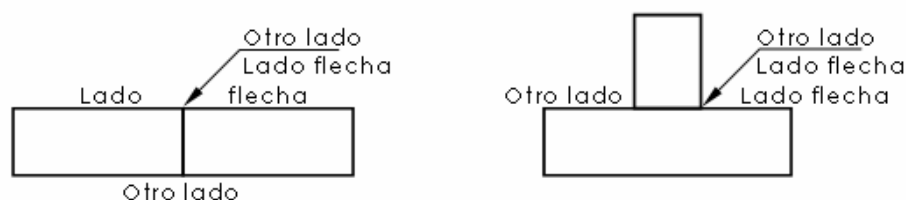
Localización estándar de elementos de la simbología de soldadura
